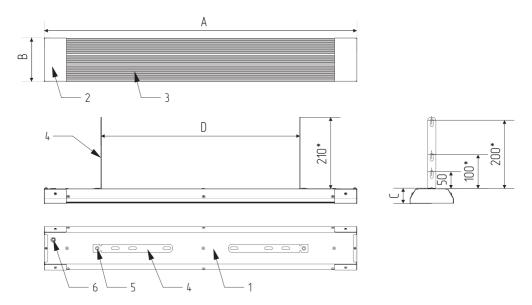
Внешний вид и элементы конструкции обогревателя 60-0010, 60-0011.
